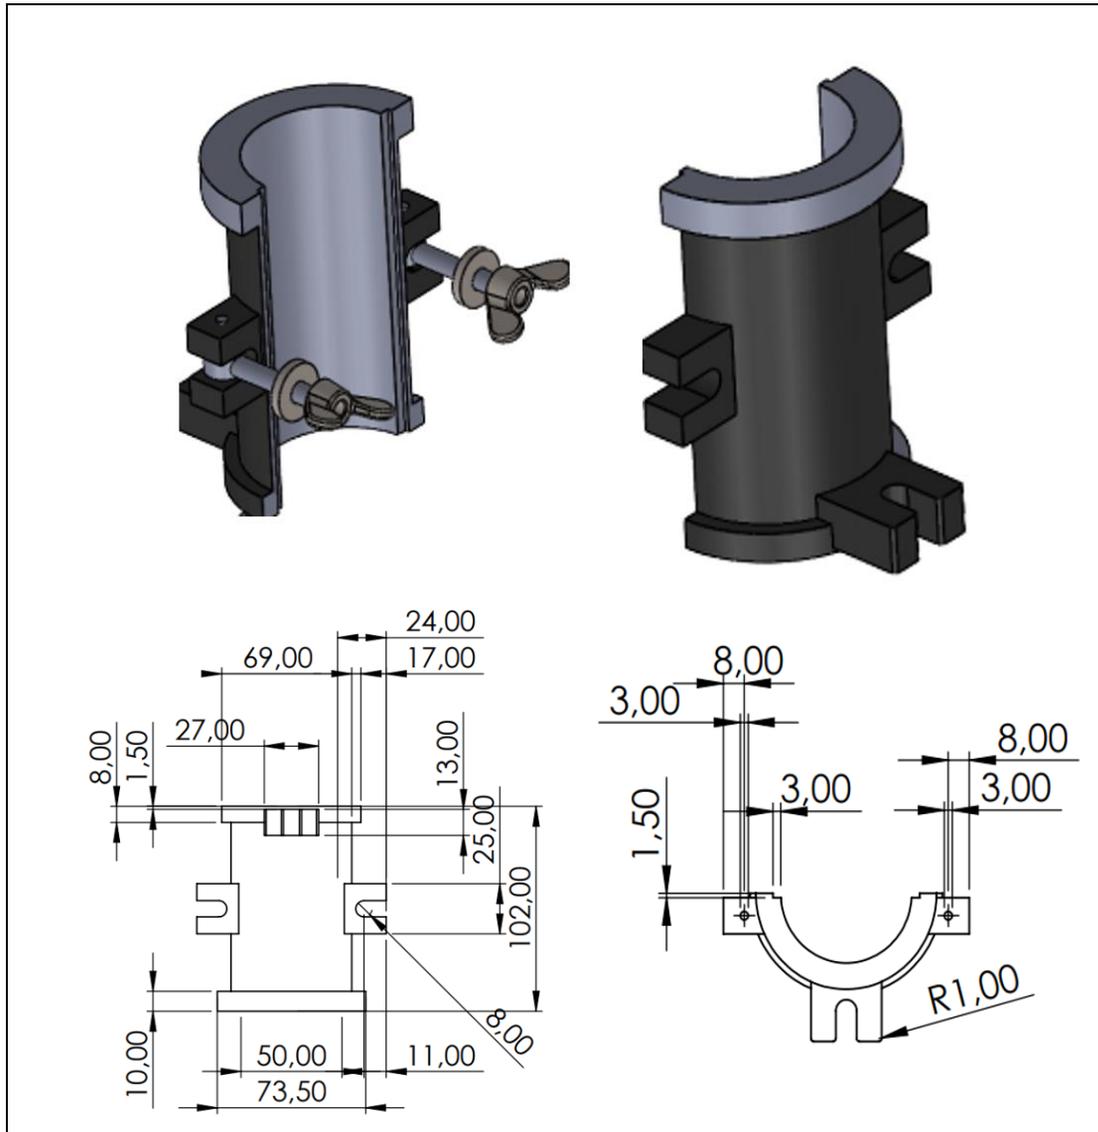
Esquema por partes – molde del equipo de compactación miniatura
